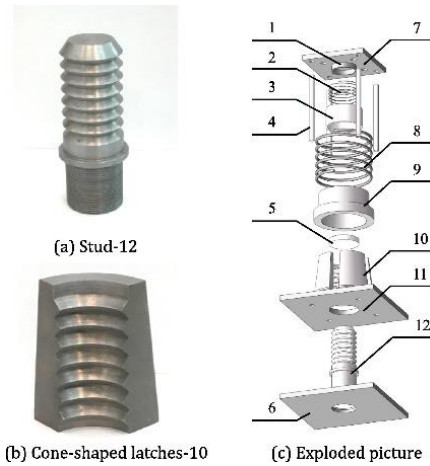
Ardgerilmeli bağlantının detayları (Sanches et al. 2018)
